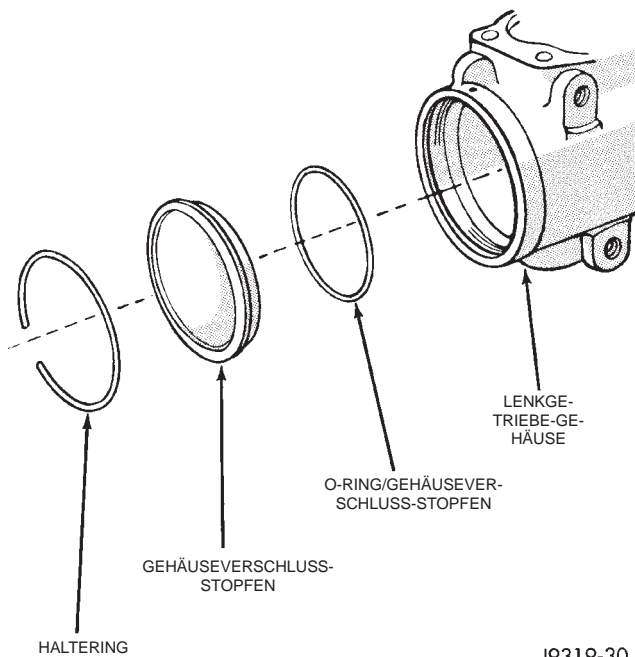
Gehäuseverschluss-Stopfen, Dicht- und Haltering
